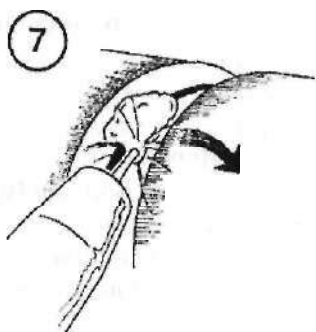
Техника сварки корневого шва неповоротных
